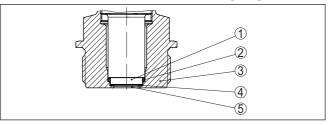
Frontbündiger Einbau der Messzelle (Beispiel: Gewinde G11/2)
